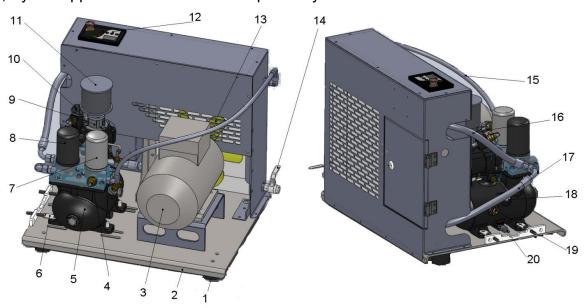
Компрессорная установка ДЭН-4Э и ДЭН-5,5Э «ЭКОНОМ»: 1 – опора амортизационная; 2 – рама; 3 - электродвигатель приводной; 4 - клапан минимального давления; 5 – компрессорный модуль; 6 – натяжное устройство ременной передачи; 7 – сепаратор-ловушка;; 8 – фильтр масляный; - 9 – клапан впускной; 10 – электроуправление впускным клапаном; 11 - фильтр воздушный; 12 – панель управления; 13 - вентилятор; 14 – кран раздаточный; 15 – рукав подачи воздуха в охладитель; 16 – подача масла в охладитель; 17 – выход масла их охладителя; 18 - пробка маслоналивной горловины; 19 – смотровое окно; 20 - кран слива масла.
